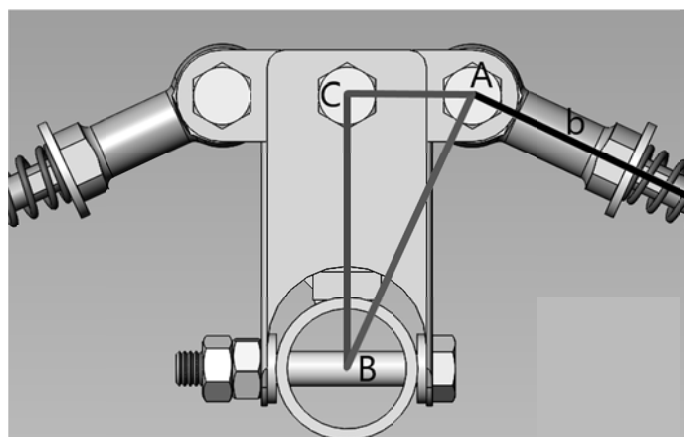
Исполнительный механизм коробки передач (общий вид)
